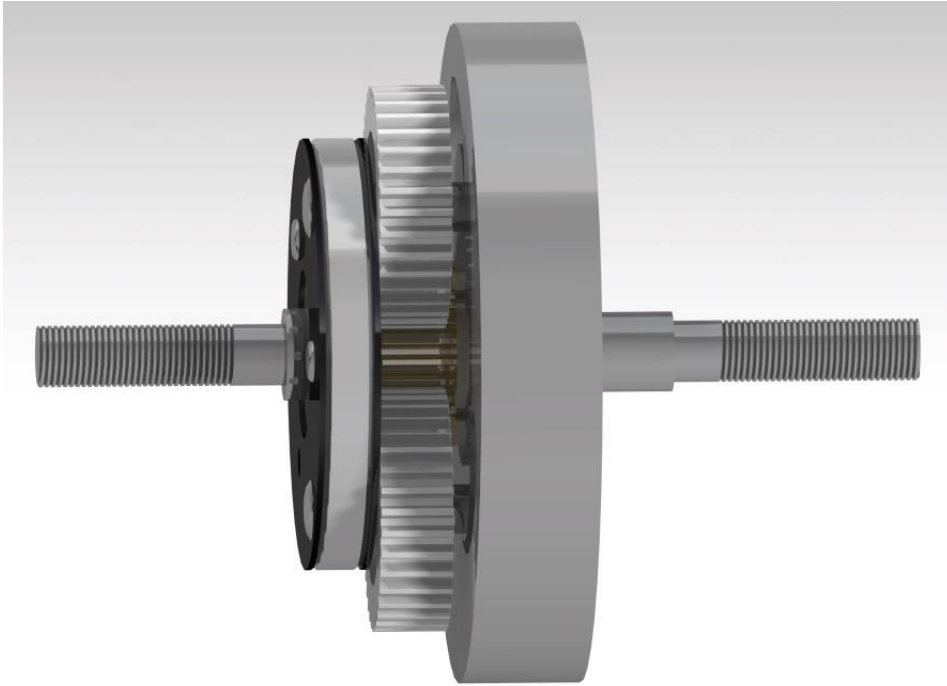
Vista del conjunto de engranajes planetarios (Fuente: elaboración propia)
